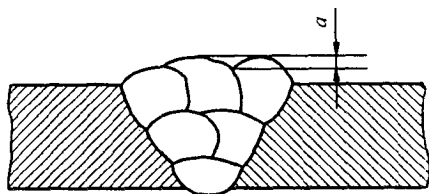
焊缝表面下凹深度(多道焊)
